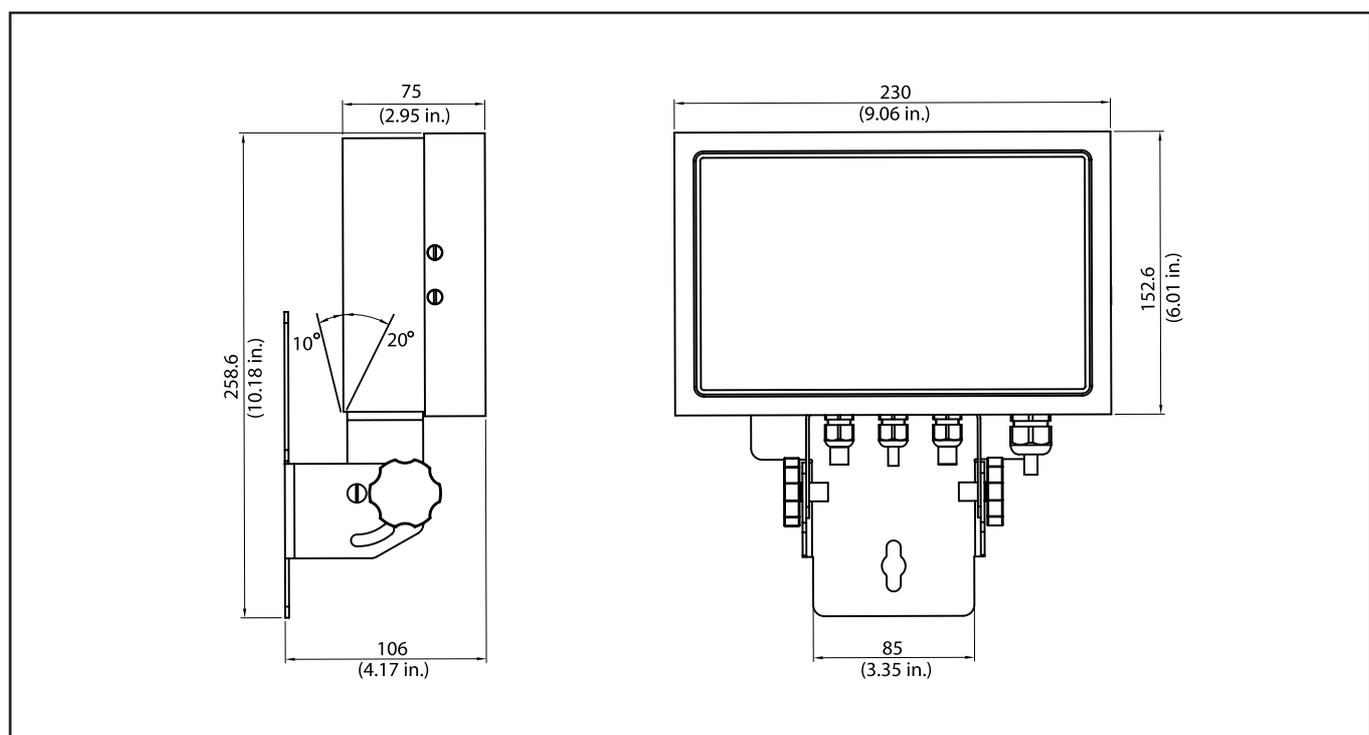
Posición de montaje del indicador CKW-55 en pared.
